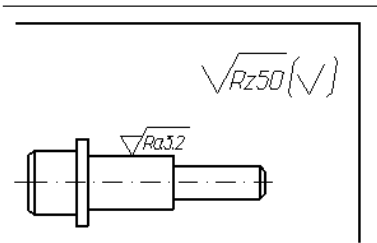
Указание шероховатости одинаковой для части поверхностей изделия
